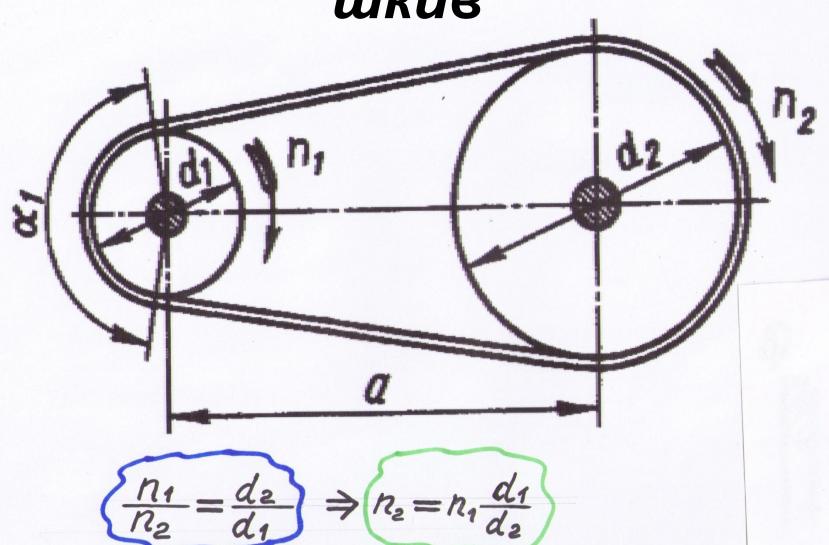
Механизм передачи движения в токарном станке по обработке древесины
